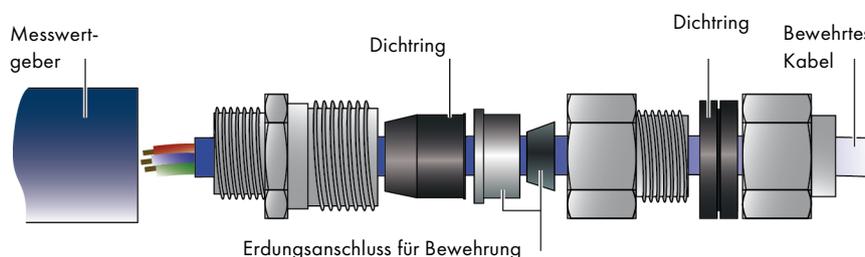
Kabelverschraubung für bewehrtes Kabel
